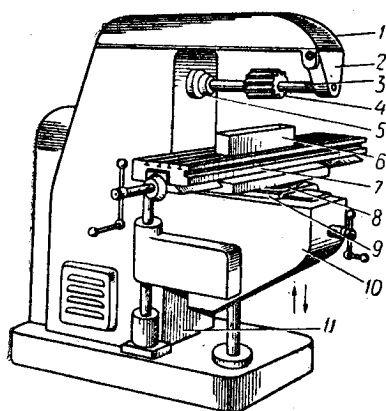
Общий вид горизонтально-фрезерного станка
